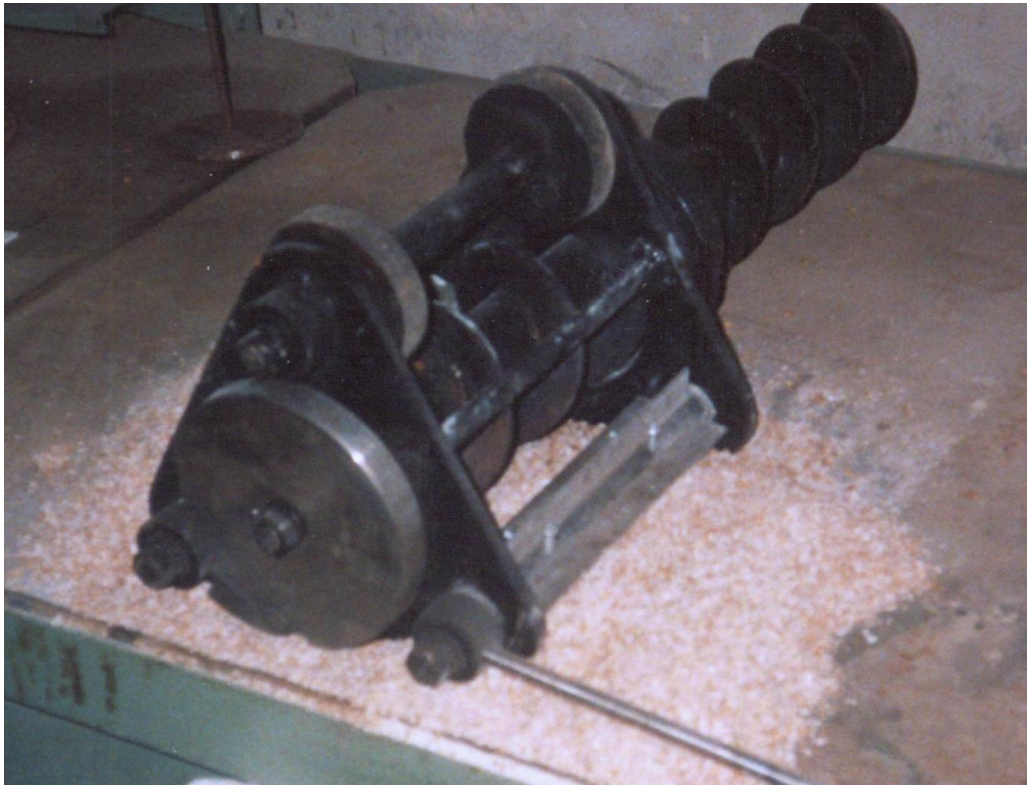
Загальний вигляд розташування на столі активного бітерного валу в корпусі патрубку
